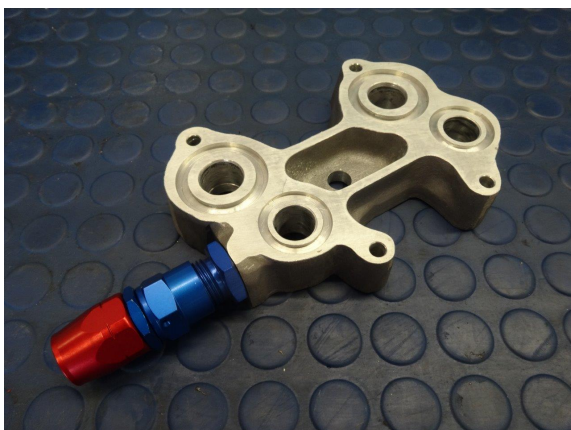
Die Adapterplatte mit Speisungsanschluss für den Accusump-Zylinder
